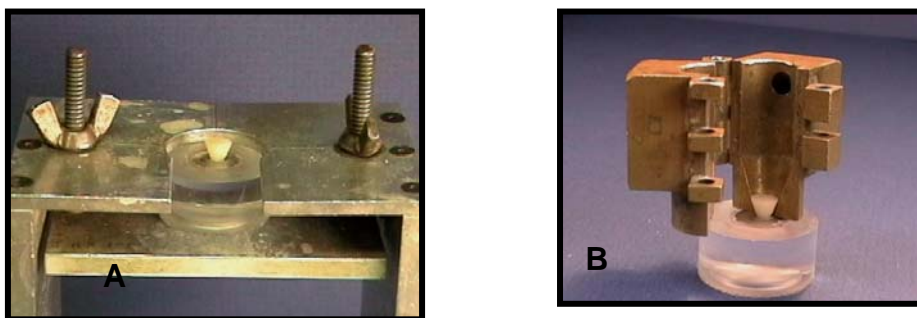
a) Base metálica para a fixação do espécime reparado na máquina de testes universal; b) dispositivo de tração sendo encaixado no espécime, antes de ser conectado com a máquina de testes universal.
